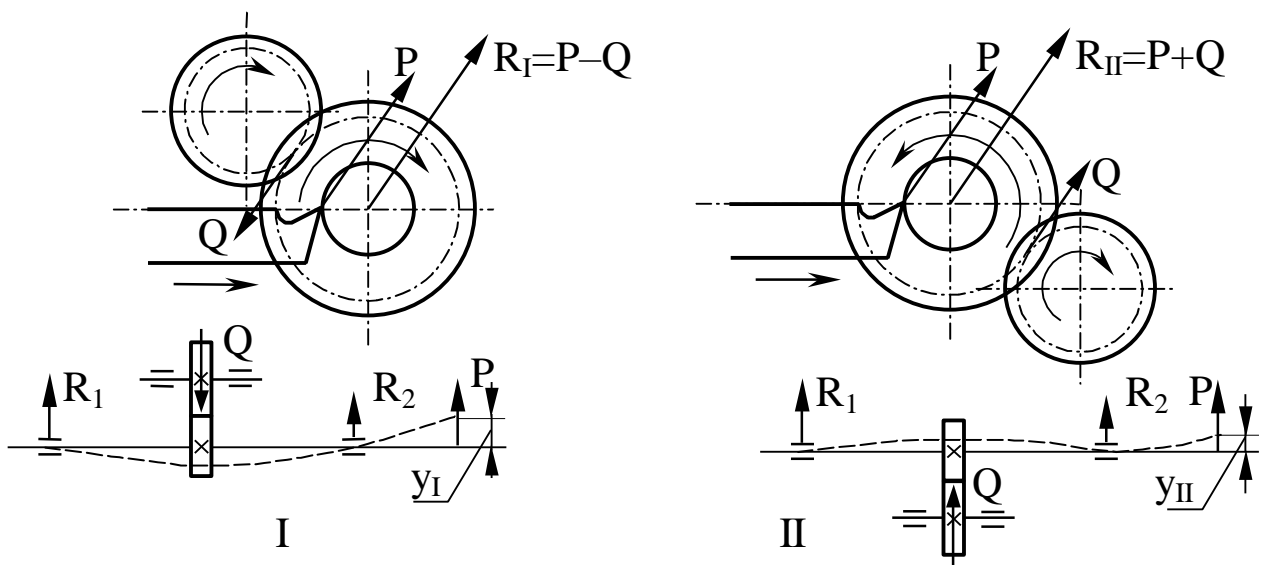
Розрахункові схеми варіантів передачі обертання на шпиндель
